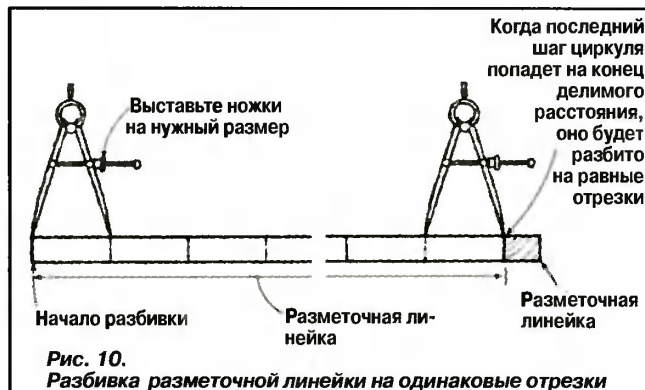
Разбивка разметочной линейки на одинаковые отрезки
